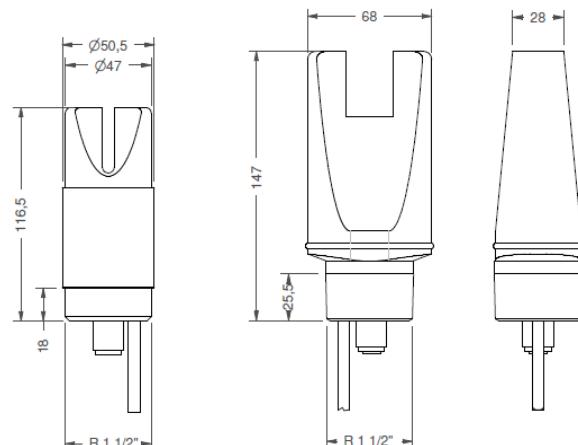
Abmessungen soli::lyser (Maße in mm)
